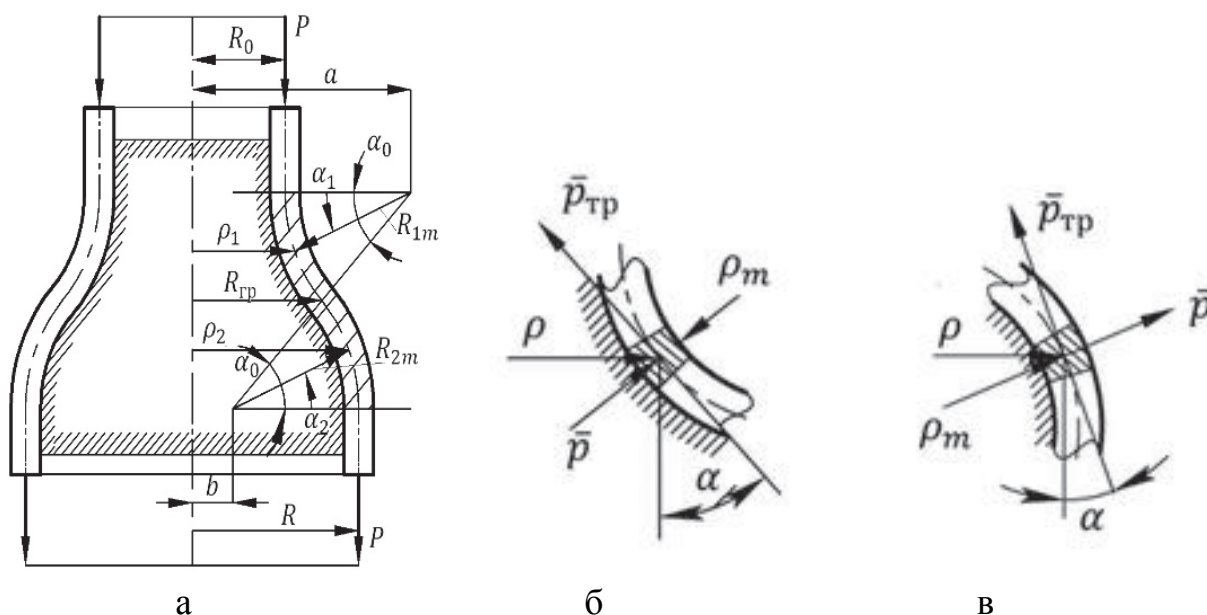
Общий случай раздачи и протяжки трубной заготовки
